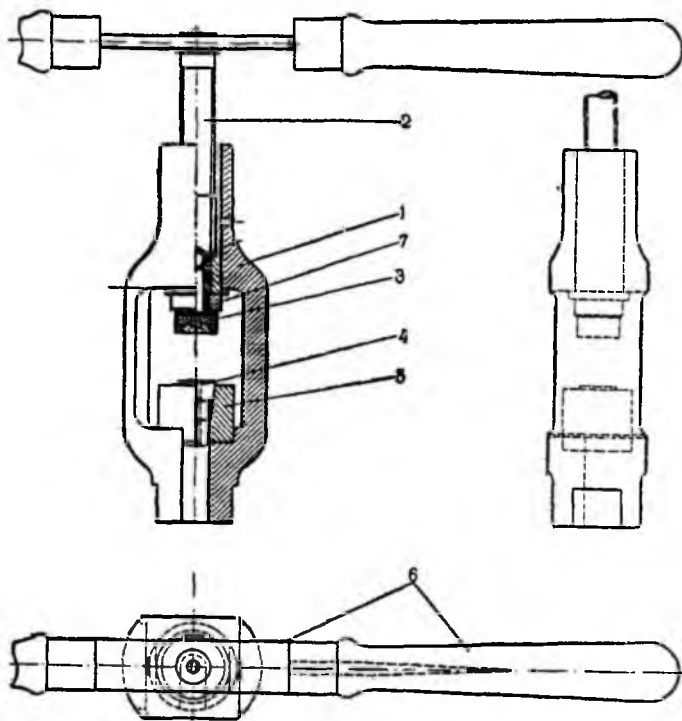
Приспособление для обсадки концов трубок высокого давления:
